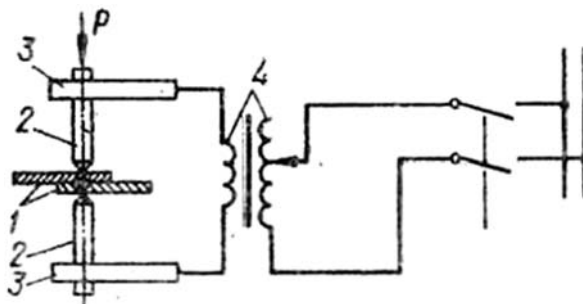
Схема точечной сварки давлением
